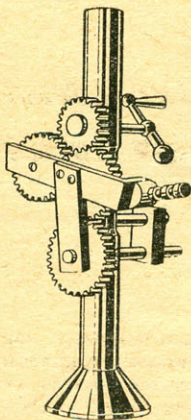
Действующая модель кинематической схемы передачи движения от шпинделя к суппорту токарного станка.
